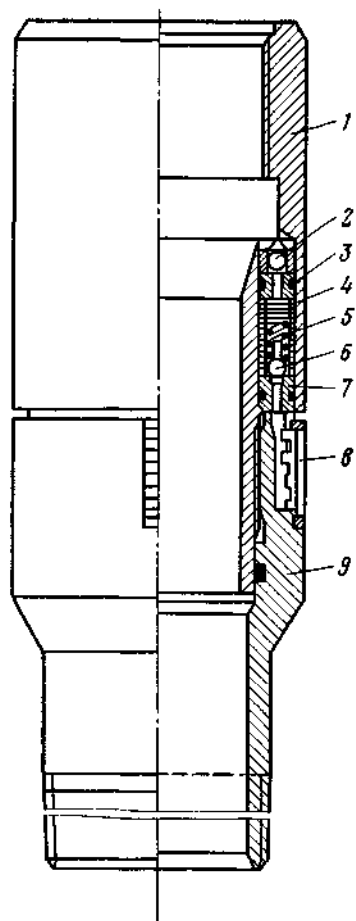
Ингибиторный клапан типа КИНГ:
